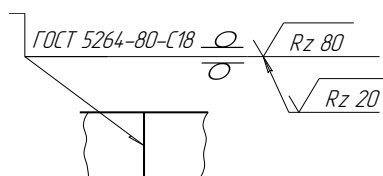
Условное обозначение стыкового сварного шва
